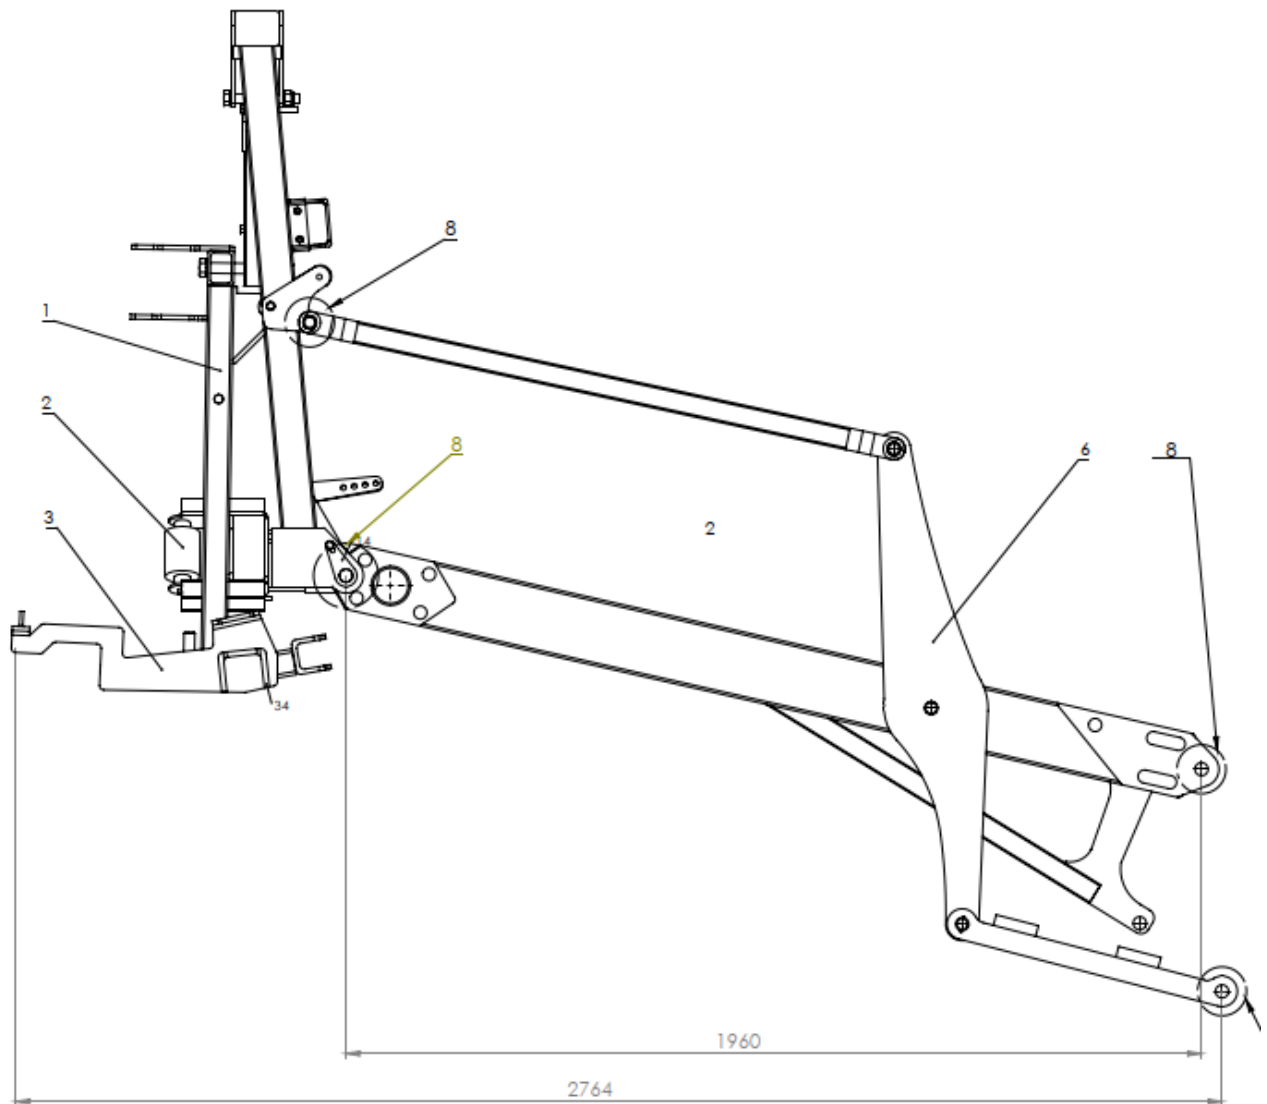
Механізм піднімання-опускання та контролю висоти штанги обприскувача John Deere 732 (вид збоку)
